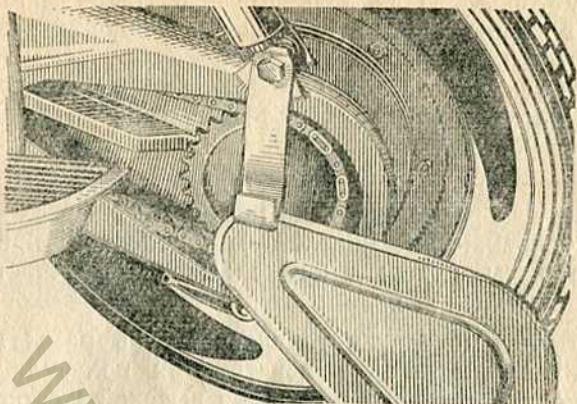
Съемная крышка в кожухе, закрывающем заднюю цепную передачу.
